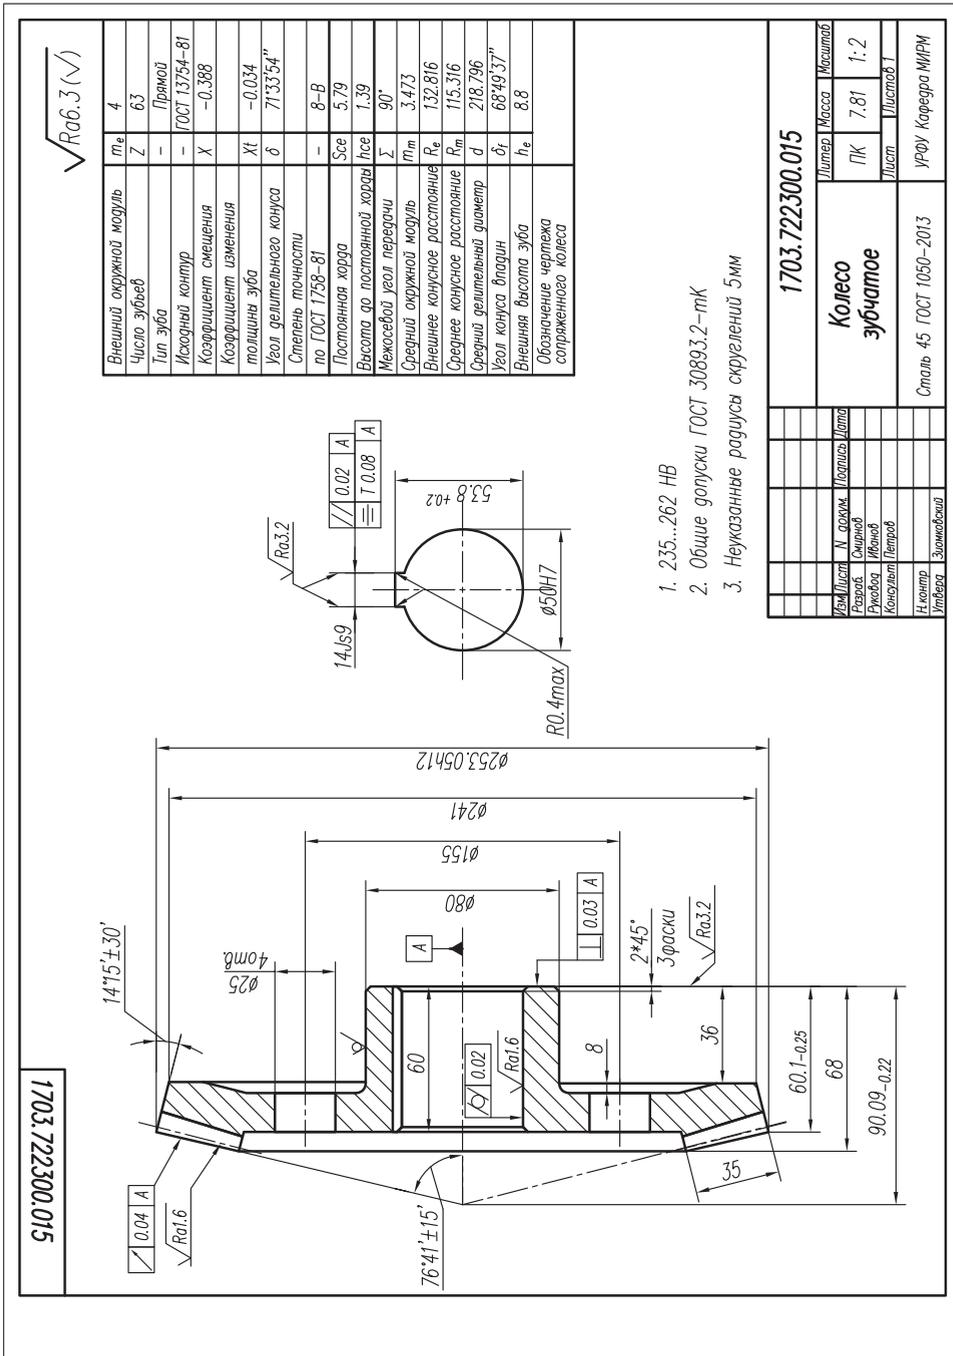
Рабочий чертёж зубчатого конического колеса
